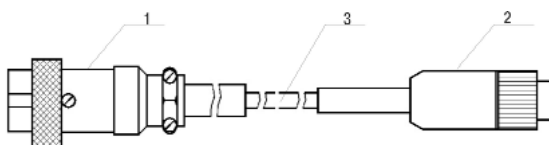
Кабель удлинительный для поверки ЗВЛМ
